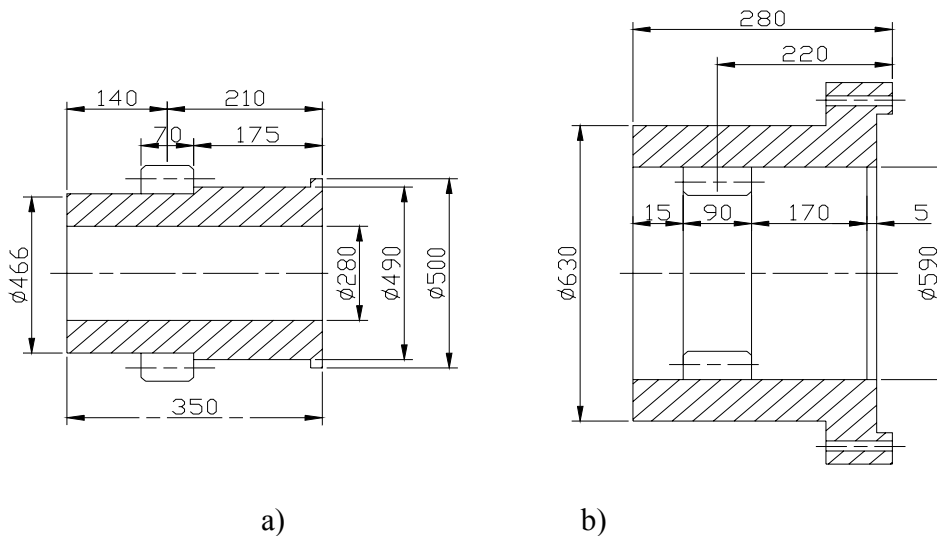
Dimensiones fundamentales de las partes del acoplamiento
